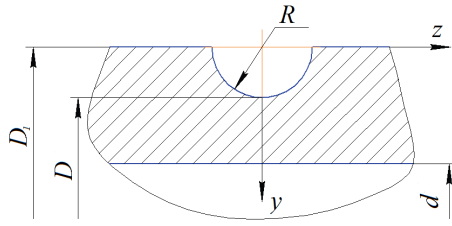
Цилиндрический образец с надрезом полукруглого профиля
